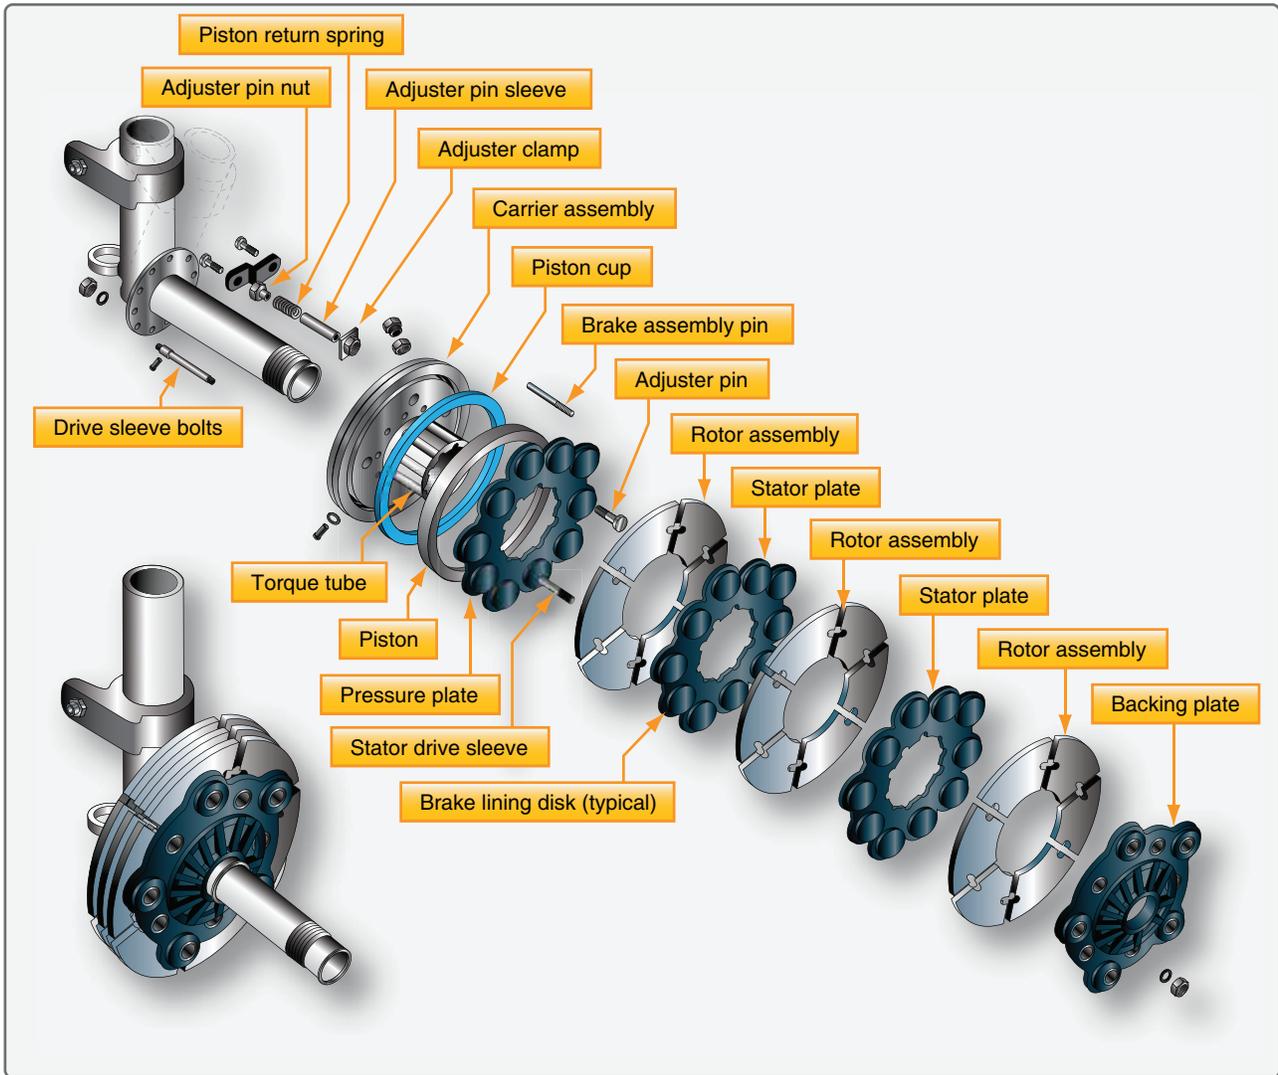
Vista aumentada e em detalhe de freios do rotor segmentados.
